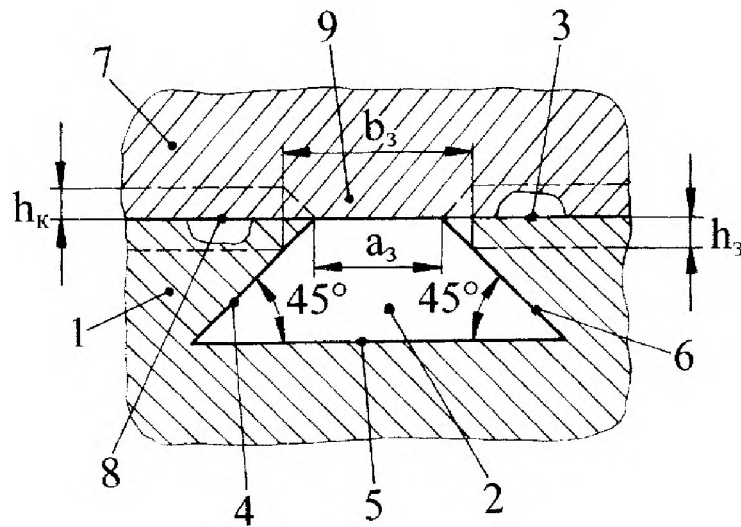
Схема пари тертя зразка і контрзразка для випробування матеріалів на знос: 1 – зразок; 2 – паз зразка; 3, 8 – робочі поверхні зразка і контрзразка; 4, 6 – бокові грані паза зразка; 5 – дно паза зразка; 7 – контрзразок; 9 – виступ контрзразка.
